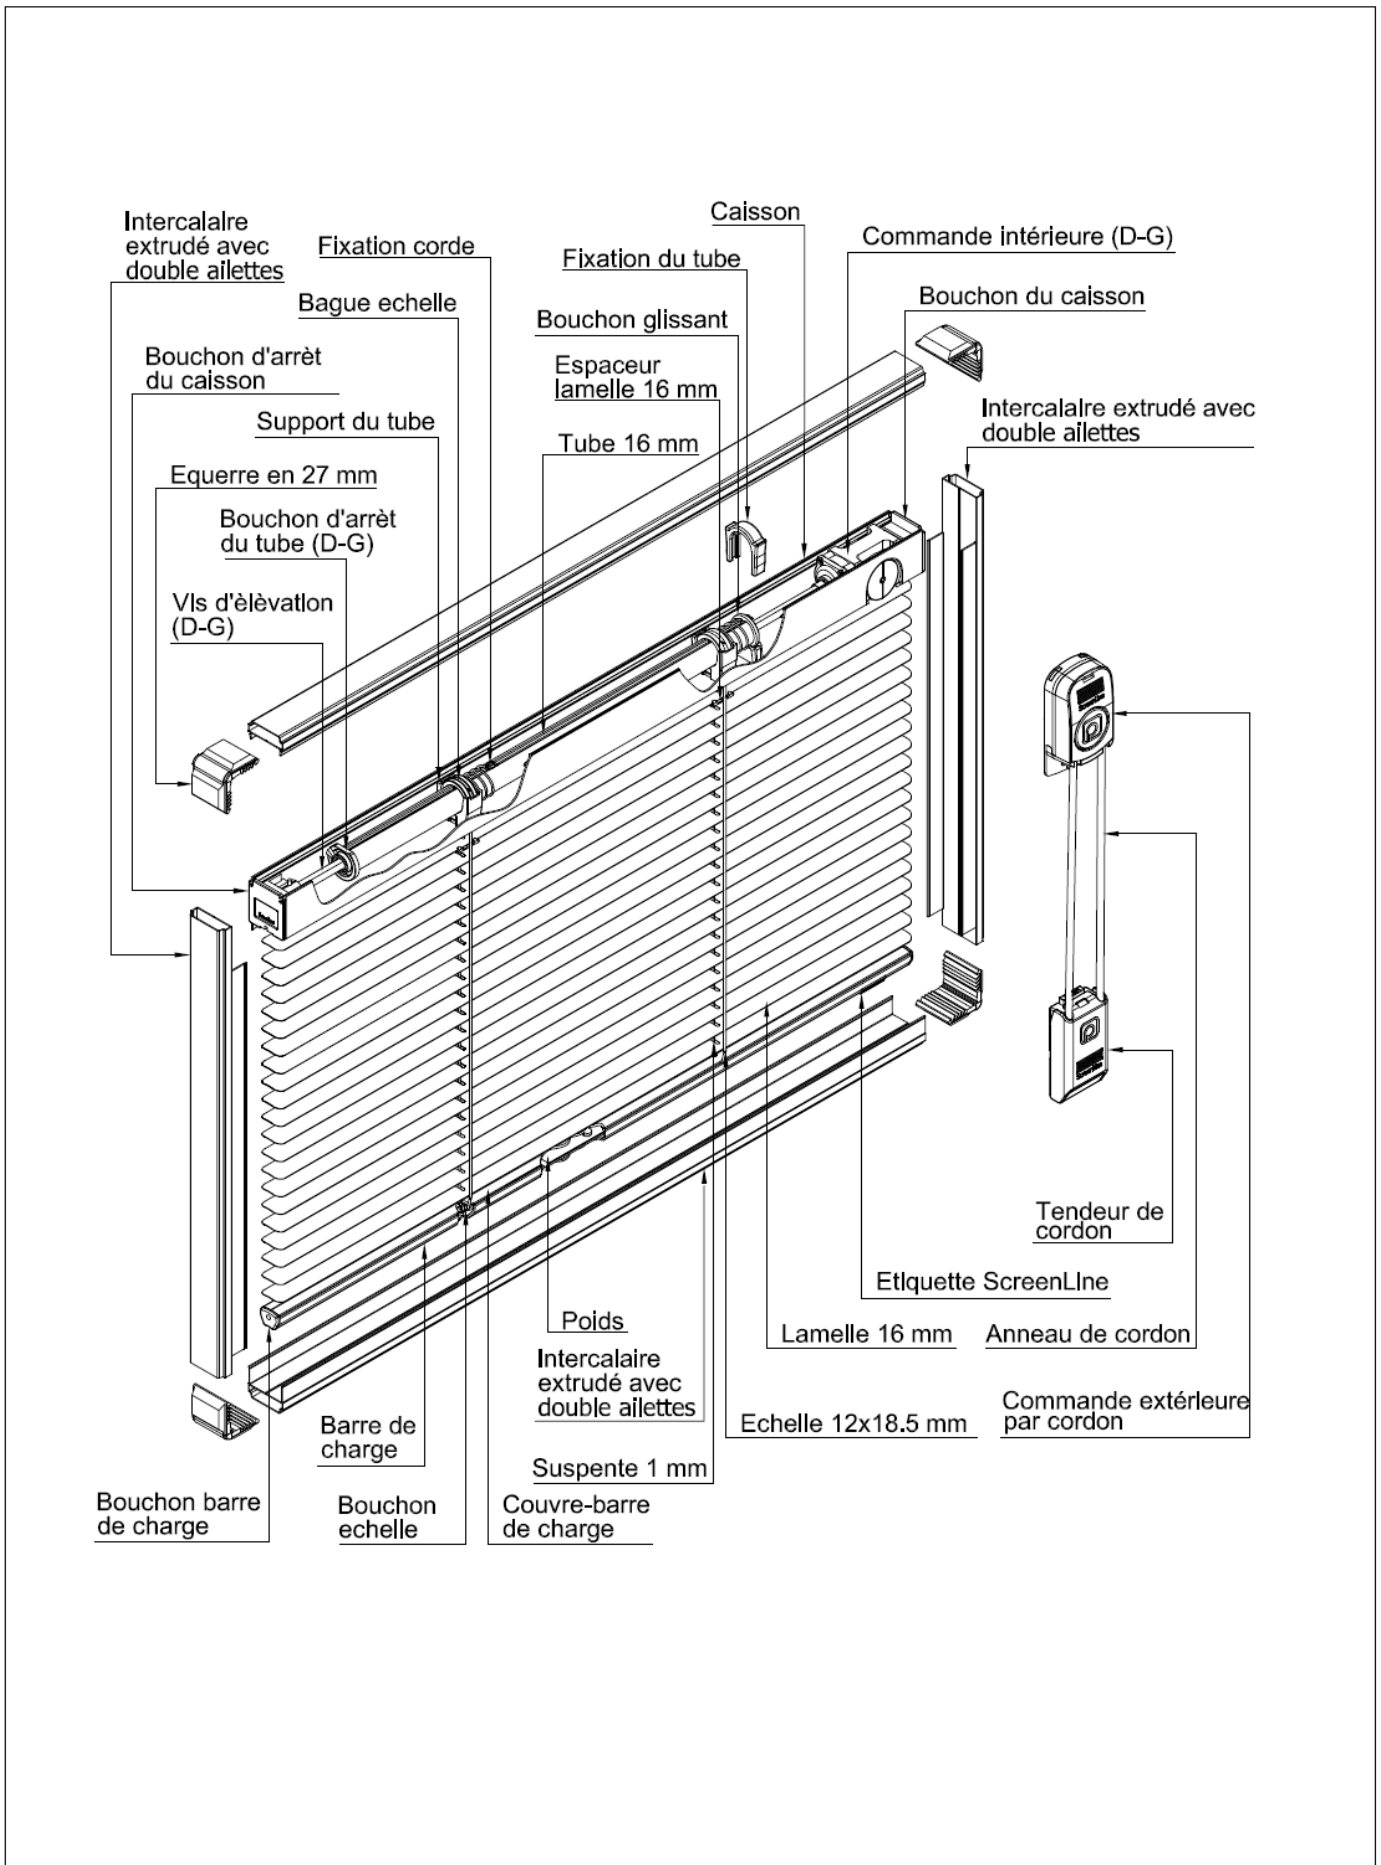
Vue d'ensemble éclatée - Store en position relevée
